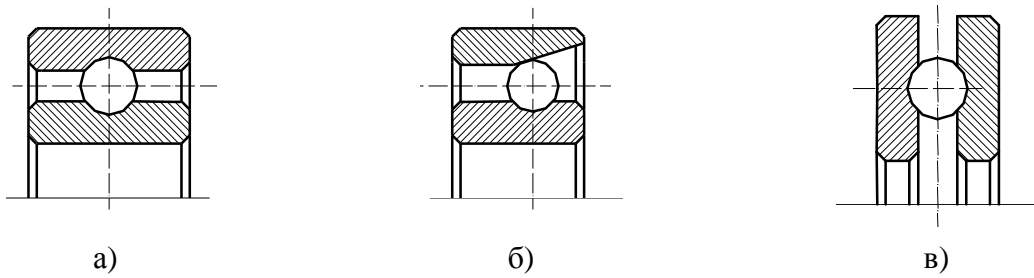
Види підшипників: а – радіальні; б – радіально-упорні; в – упорні
